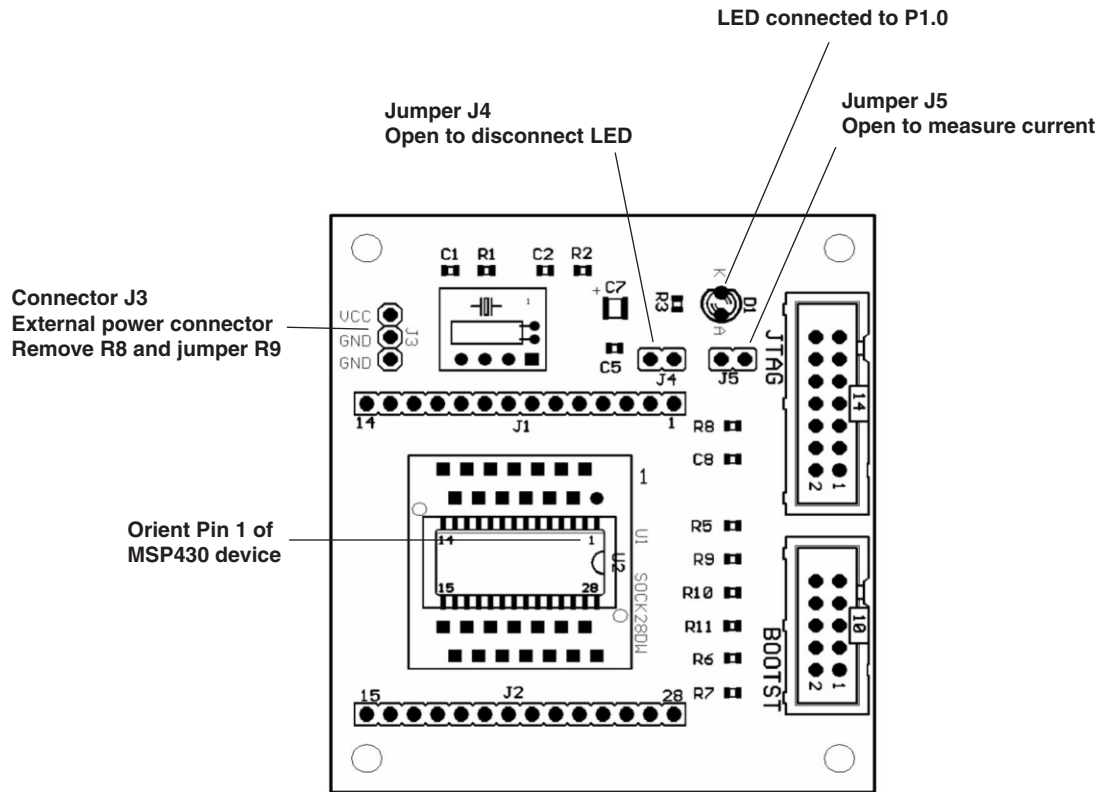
MSP-TS430DW28 目标插座模块, PCB
